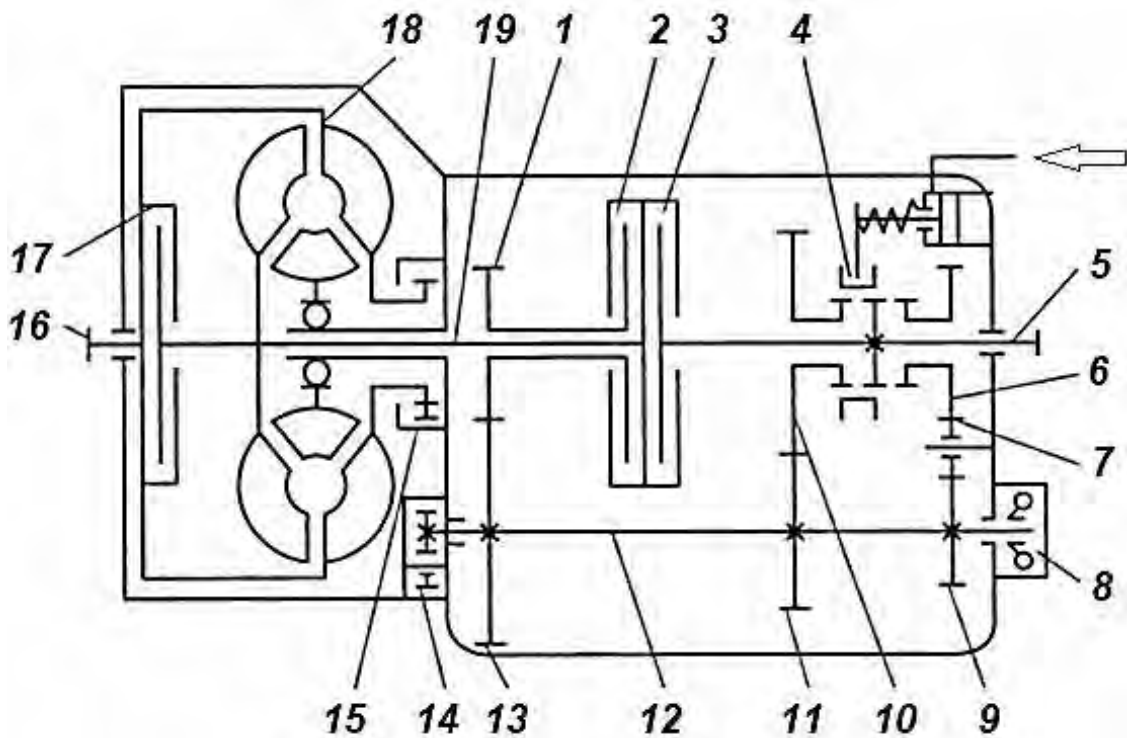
Принципова схема двоступінчастої трьохвальної гідромеханічної коробки передач з шестернями постійного зачеплення і гідропідтискними муфтами [13]:
